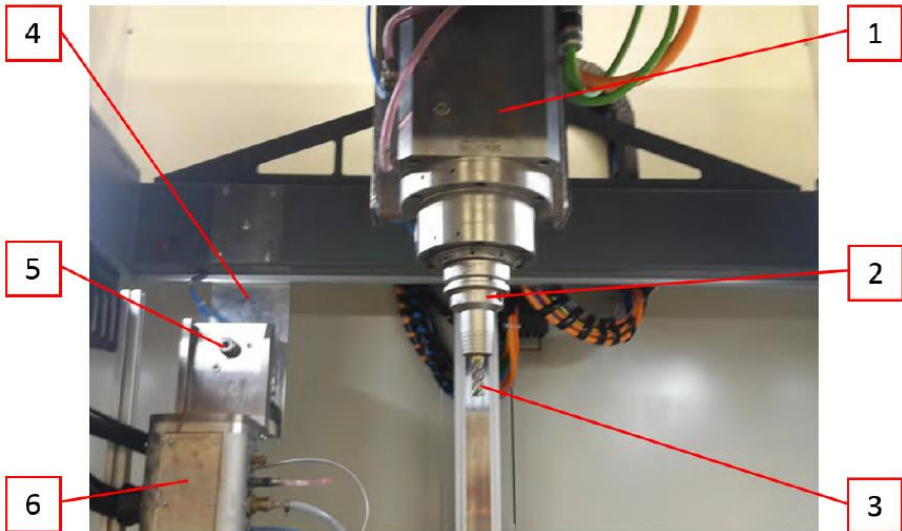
Fräsmodul der GTarc+, 1 Werkzeugspindel, 2 Werkzeughalter, 3 Schaftfräser, 4 Ablageplatz für Schweißbrenner, 5 Aufnahme für Spannsystem, 6 Schweißbrenner
